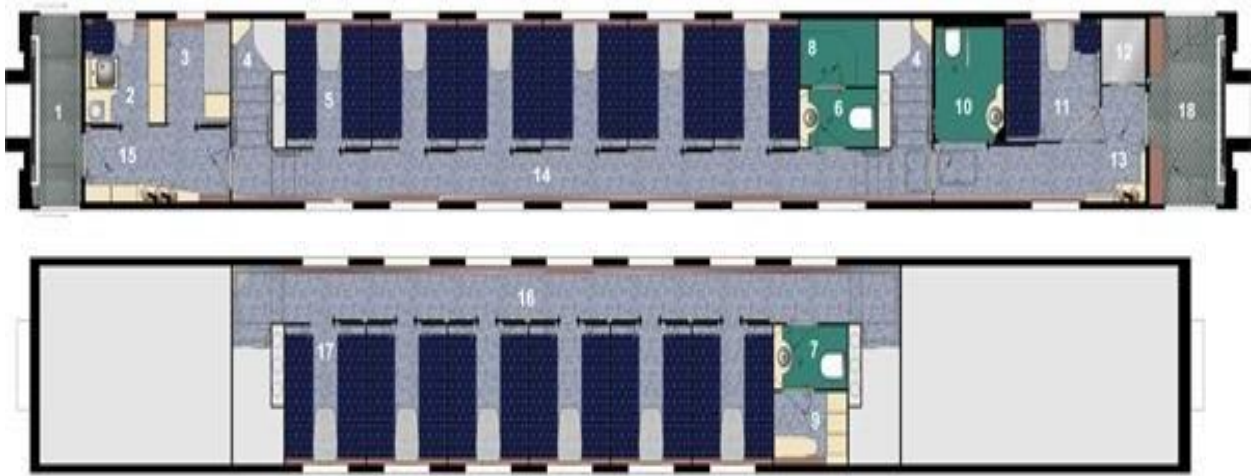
Схема розташування приміщень двоповерхового штабного вагона
